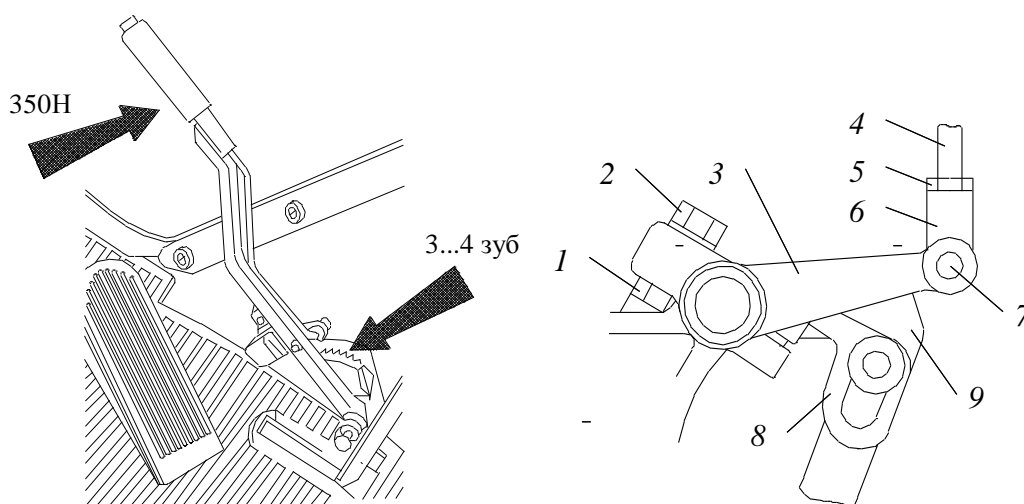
Схема проверки и регулировки стояночного тормоза:
